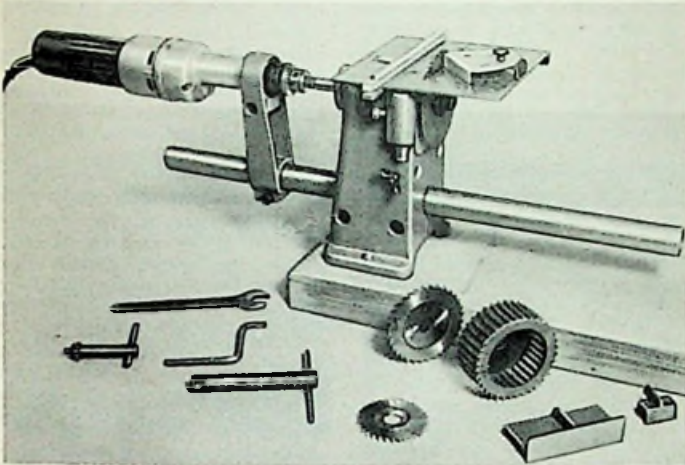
Der Säge- und Hobeltisch mit verschiedenen Werkzeugen
